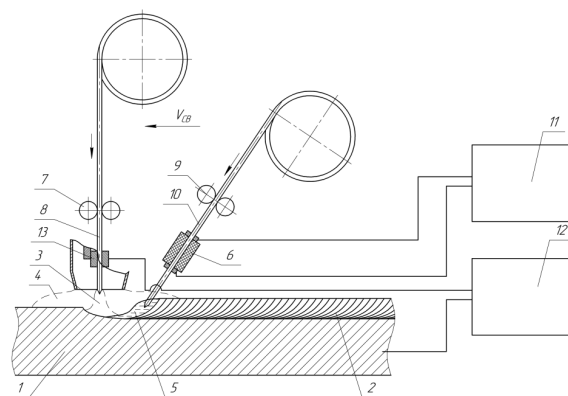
Схема установки: 1 – ОМ, 2 – МШ, 3 – дуга, 4 – защитный газ, 5 – сварочная ванна, 6 – подогревающий элемент, 7 – механизм подачи проволоки, 8 – проволока, 9 – механизм подачи ДГП, 10 – ДГП, 11 – источник питания для ДГП, 12 – основной источник питания, 13 – контактный наконечник [17]
